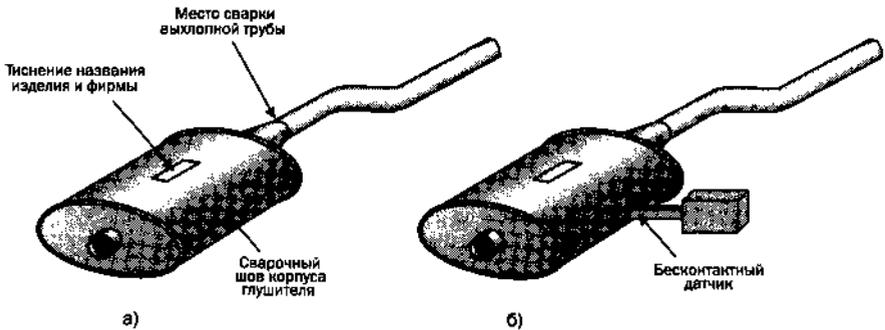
Применение устройства пока-ёкэ для контроля правильности установки корпуса глушителя перед сваркой.
